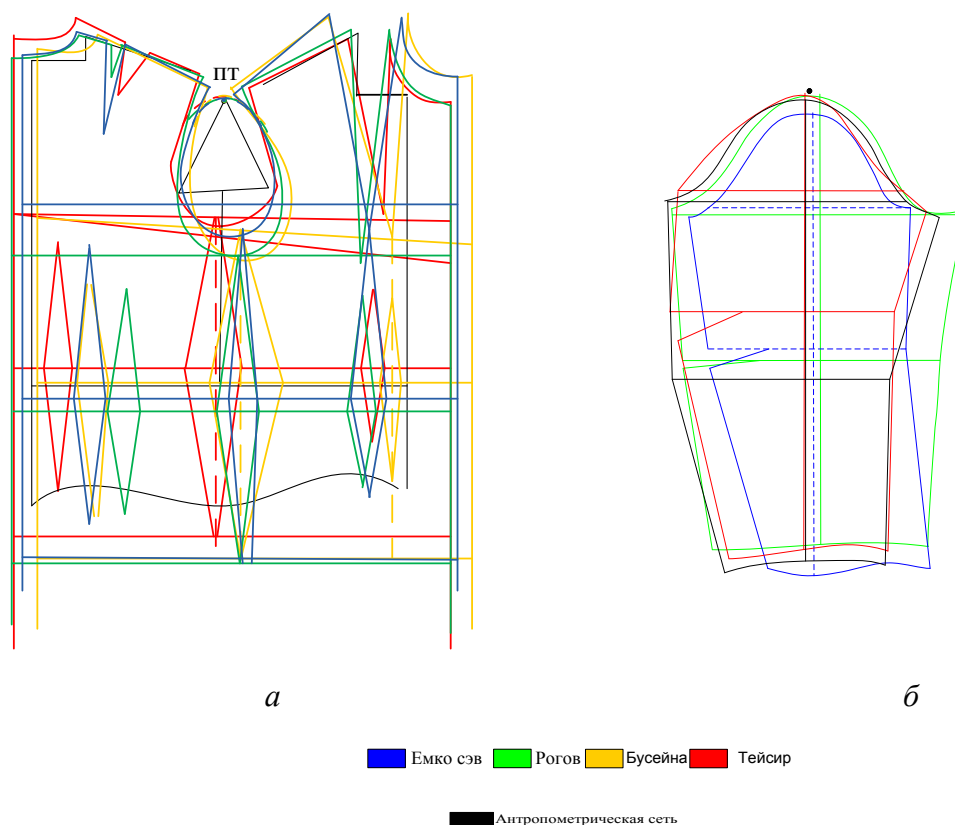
Схемы совмещения чертежей конструкций стана (*а*) и рукава (*б*) в единой плечевой точке фигуры *ПТ
